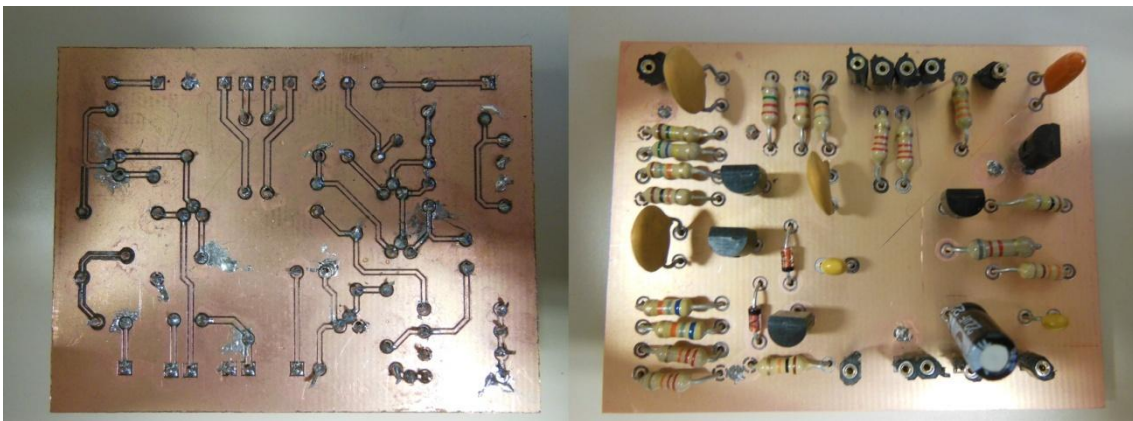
PLACA CON LOS COMPONENTES SOLDADOS
